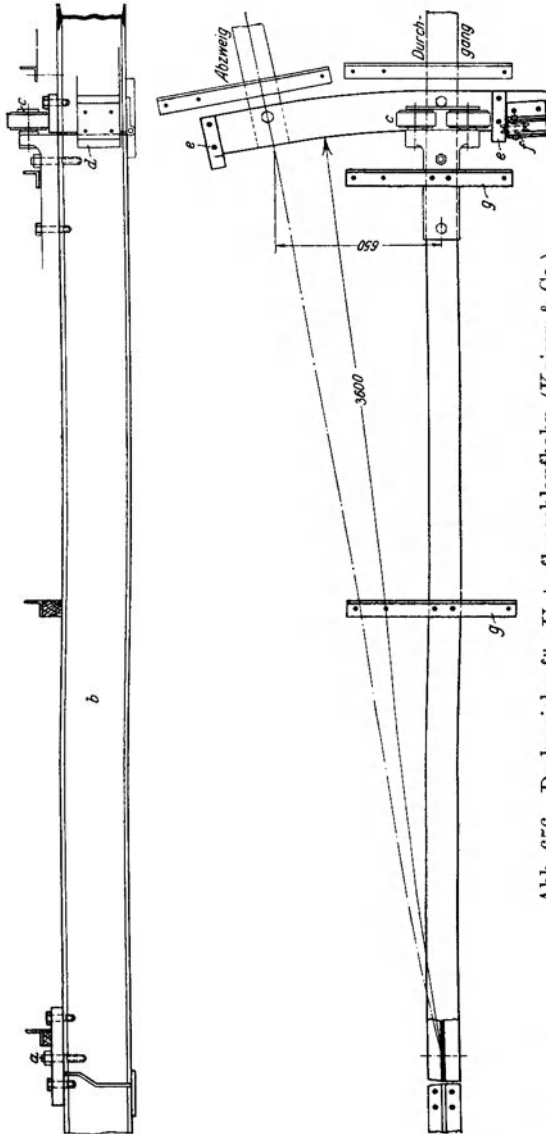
Drehweiche für Unterflanschlaufbahn (Kaiser & Co.).
